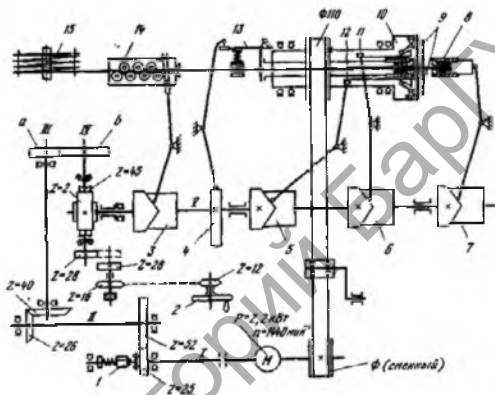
Кинематическая схема фасонно-отрезного автомата мод. 1106
